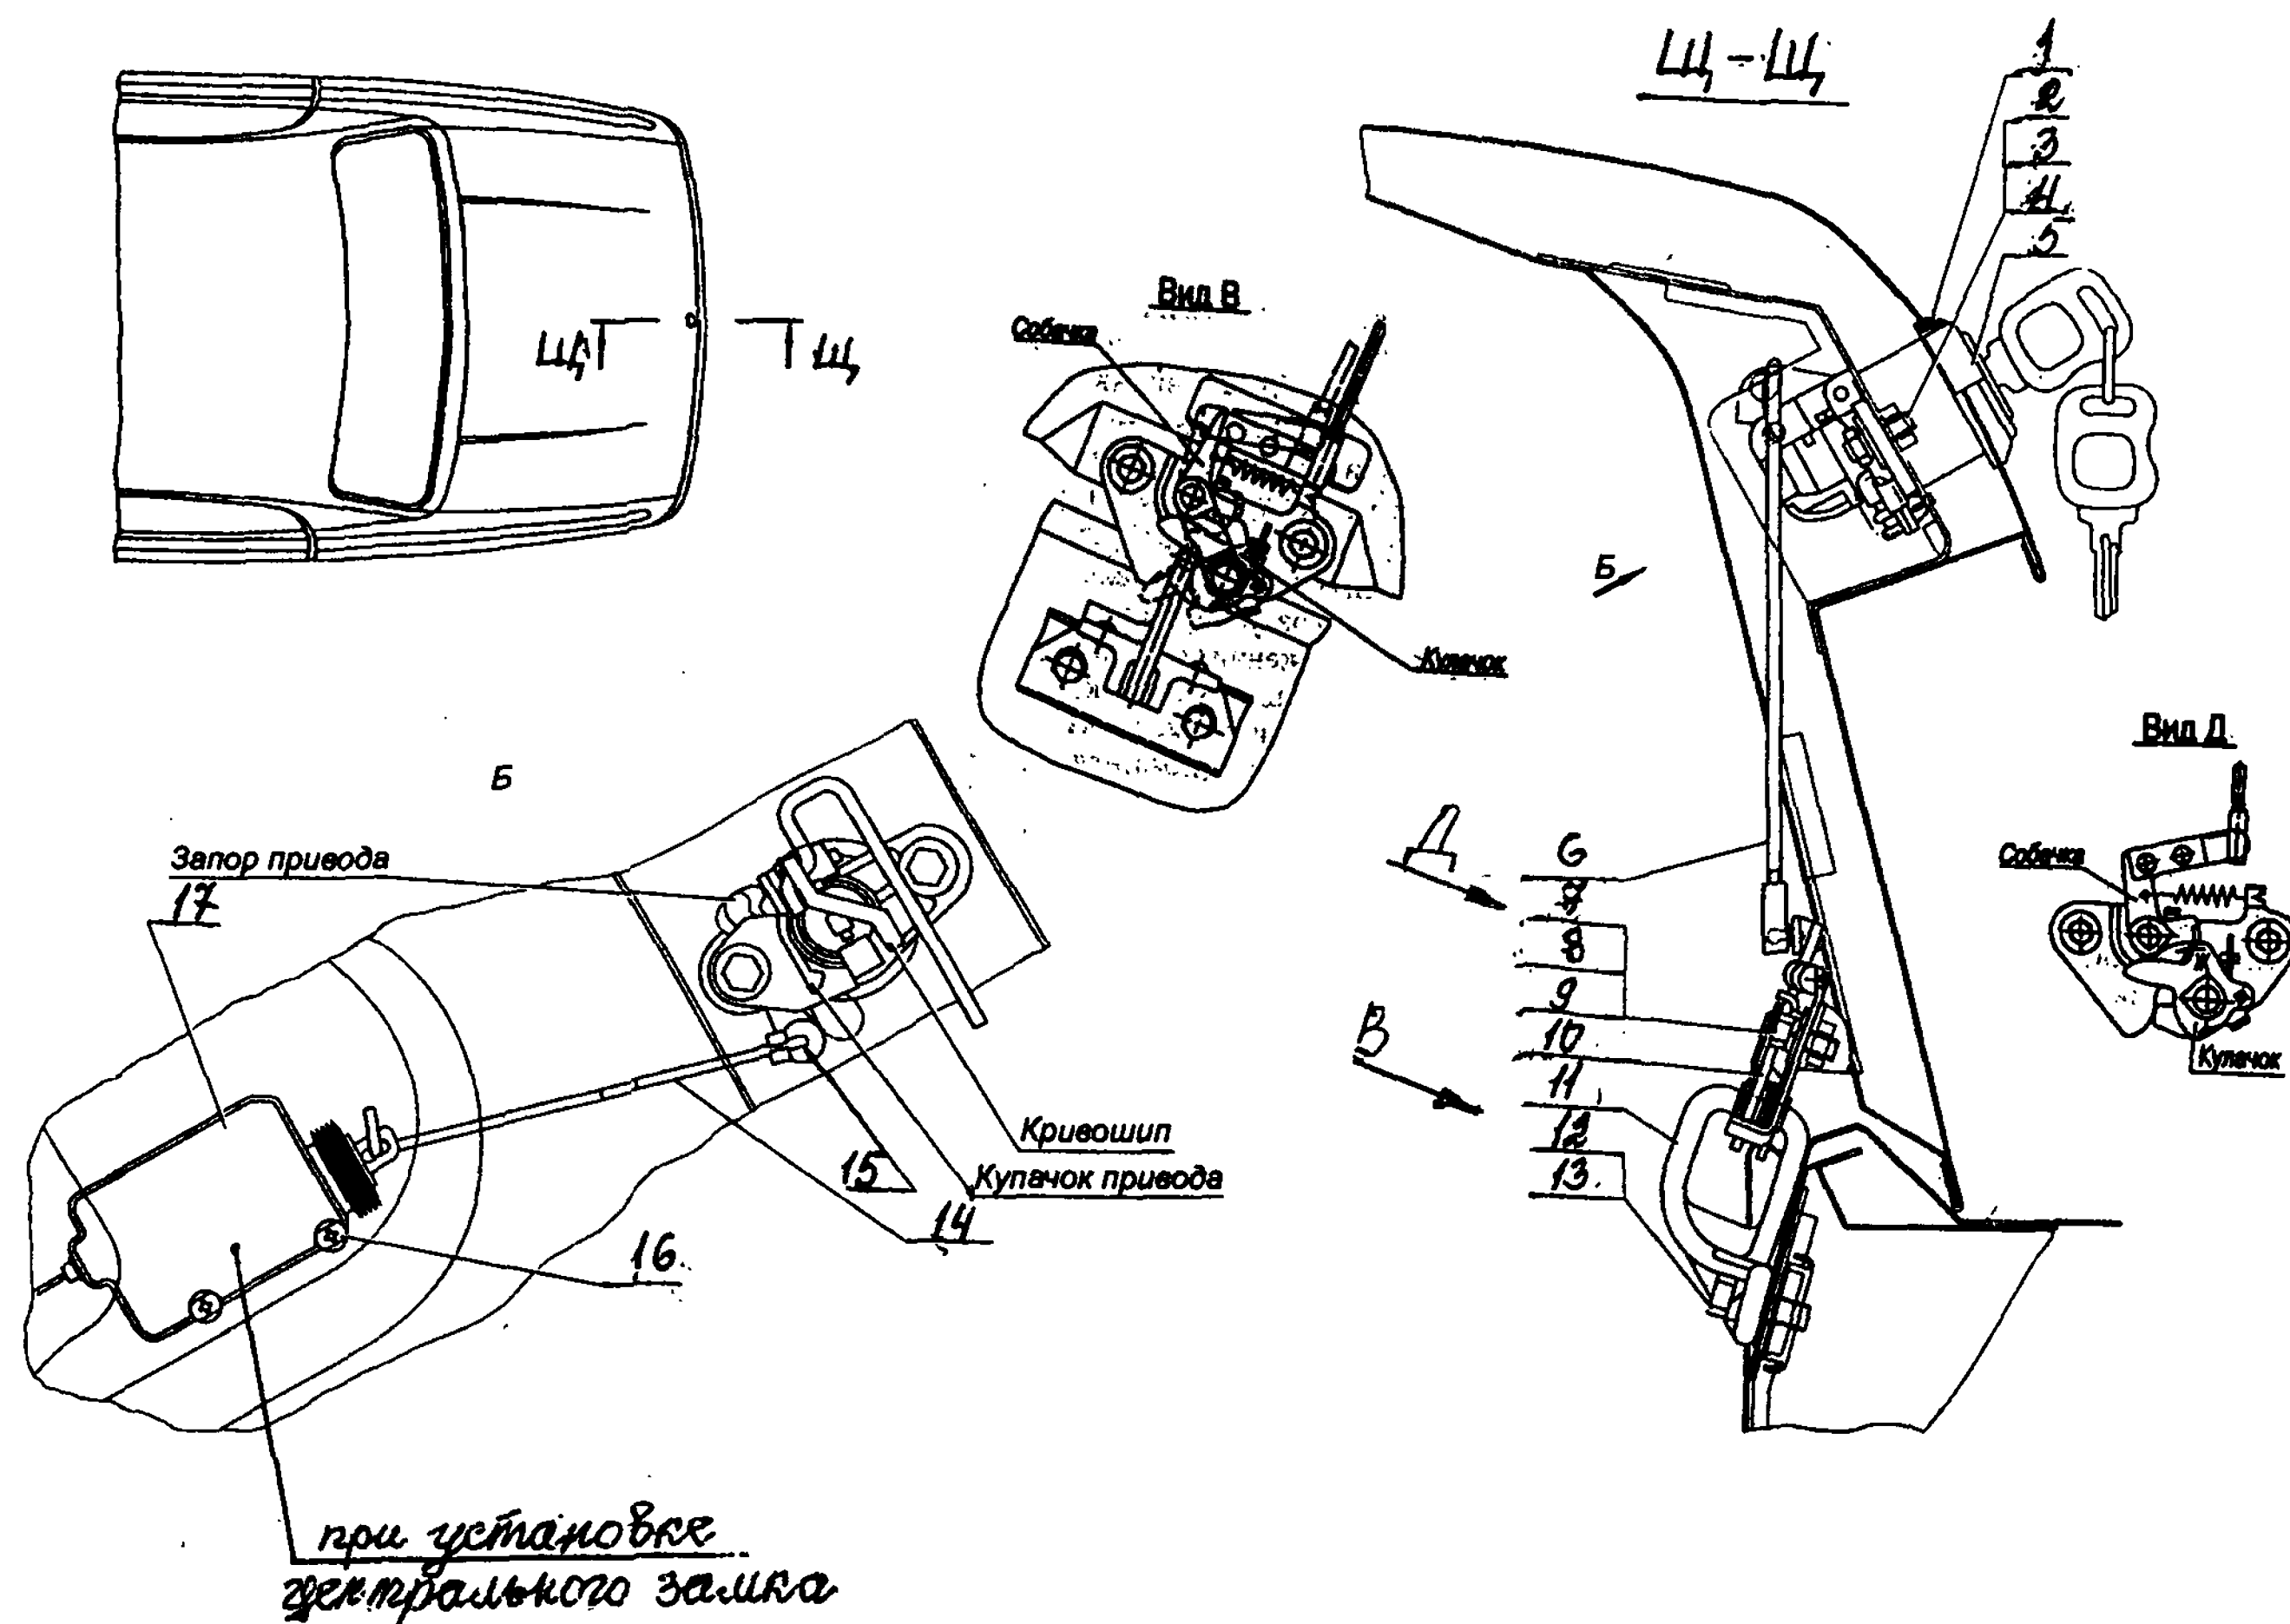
Замок багажника: 1 - уплотнитель привода; 2 - болт крепления привода; 3 - шайба плоская; 4 - шайба пружинная; 5 - привод багажника; 6 - тяга привода; 7 - болт крепления замка; 8 - шайба плоская; 9 - шайба пружинная; 10 - замок багажника; 11 - защелка замка багажника; 12 - болт крепления защелки; 13 - шайба пружинная; 14 - тяга моторредуктора; 15 - зажим тяги; 16 - винт крепления моторредуктора; 17 - моторредуктор (при наличии «центрального замка»)
